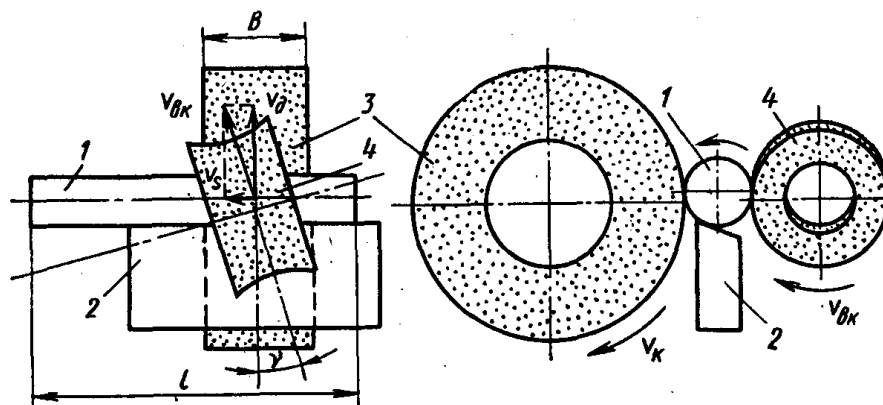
Схема бесцентрового наружного шлифования: 1 – заготовка, 2 – опорный нож, 3 – рабочий круг, 4 – ведущий круг
